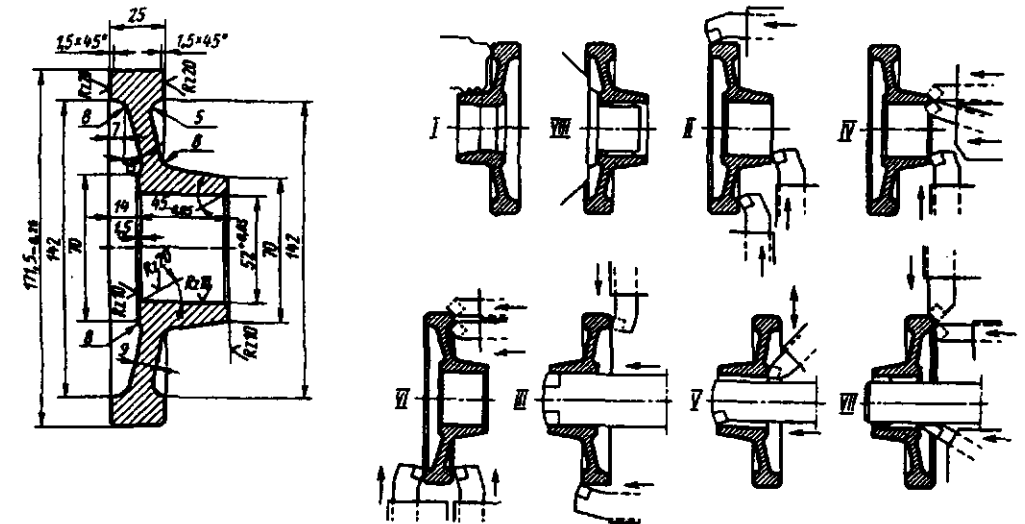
Двухиндексная наладка восьмишпиндельного полуавтомата для обработки заготовок зубчатых колес
